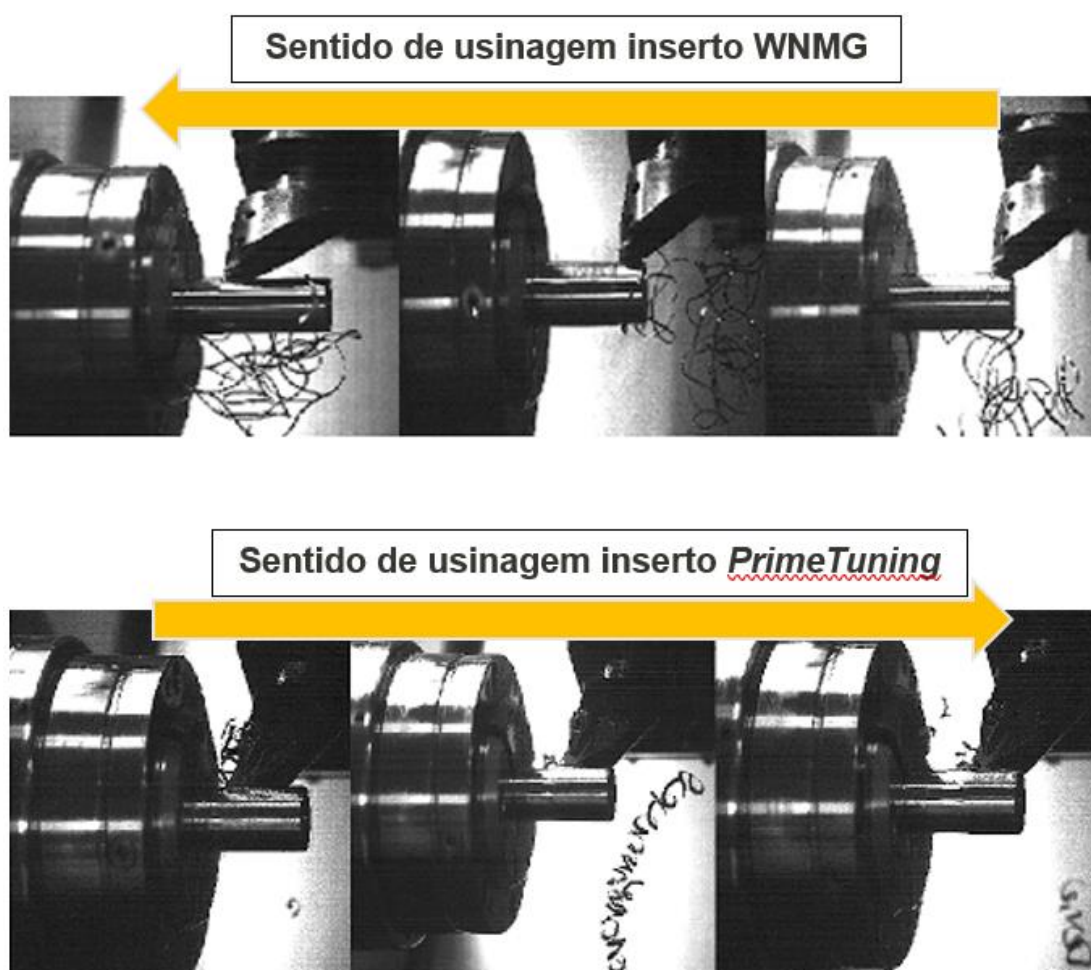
Estágios do processo de usinagem com insertos face plana
